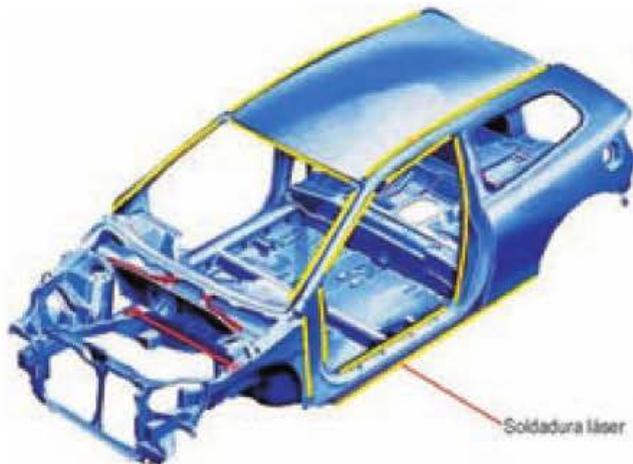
Distintas uniones por soldadura láser.
